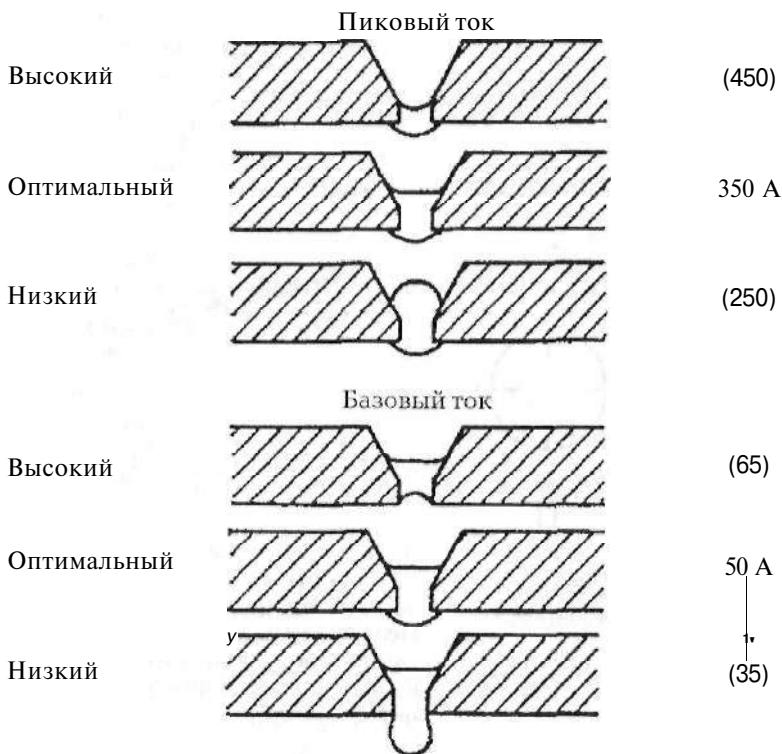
Влияние различных сварочных параметров процесса STT на форму корневого шва
